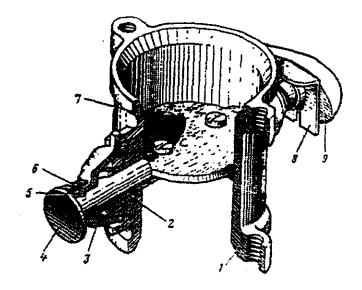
Кран 24-7604-600 включения обогрева стекол: 1-корпус; 2-втулка; 3-фиксатор; 4-ось; 5-штифт; 6-пружина: 7-заслонка; 8-чека; 9-ручка
